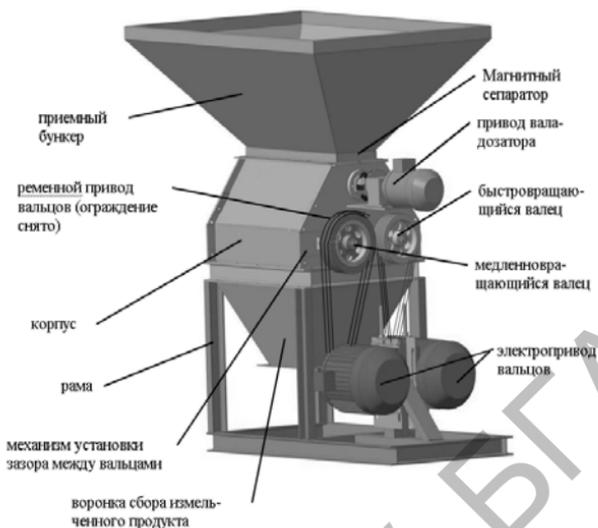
Общий вид экспериментального образца вальцовой дробилки
